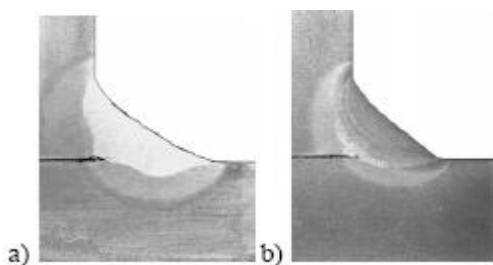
Aspecto do cordão de soldadura antes da martelagem a) e após a martelagem b)
